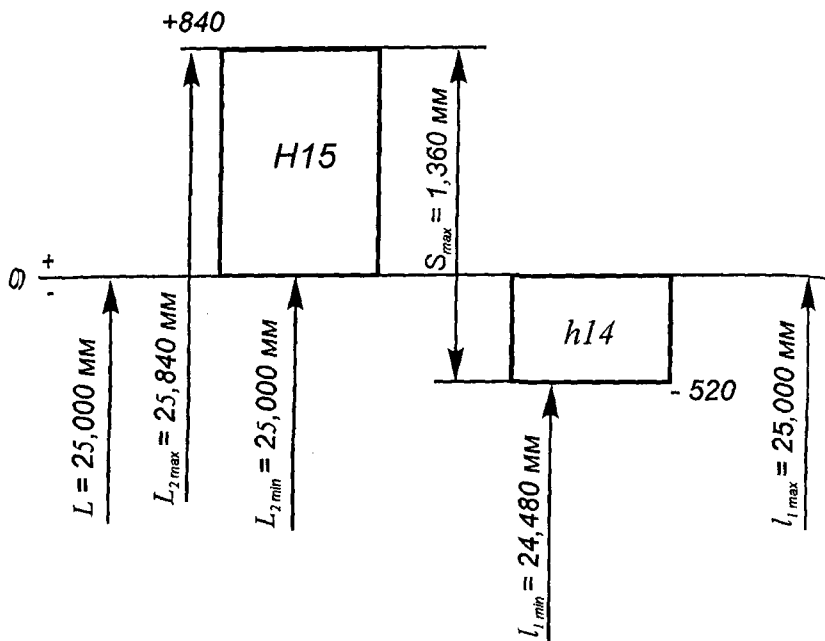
Схема расположения полей допусков по длине шпоночного паза
